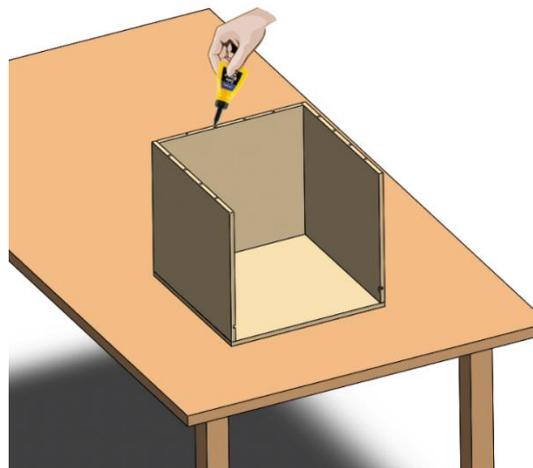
Paso 8 del ensamblaje del cajón (conjunto 2)
